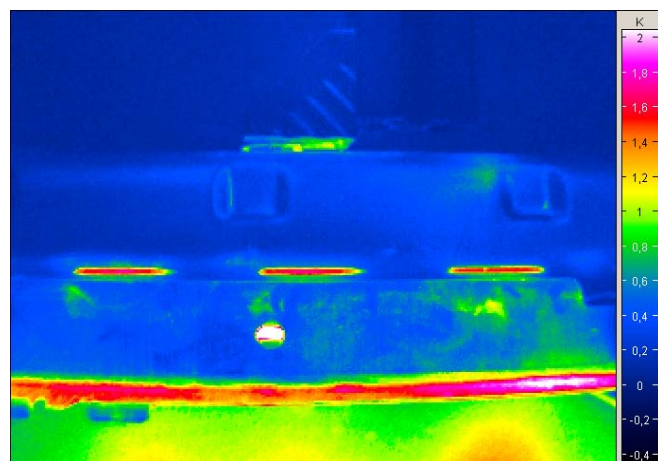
Thermografie-Prüfbild von Laserschweißnähten an einem Karosserieteil
